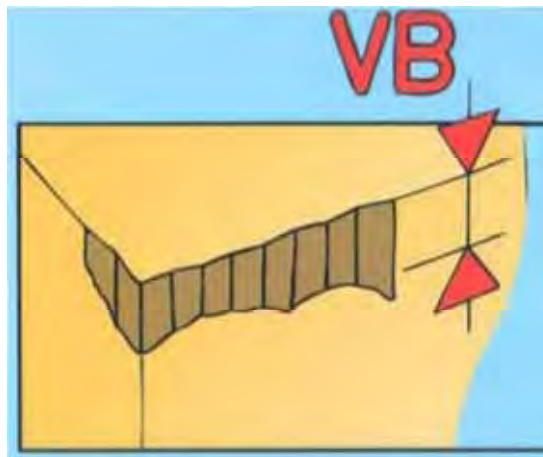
Medição do desgaste de flanco (v_b) da ferramenta, adaptado de Sandvik (2005).
